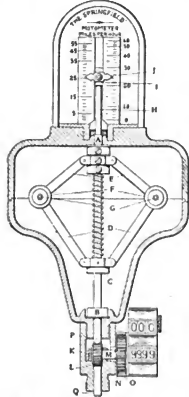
Innen-Ansicht des Springfield-Motometers.
